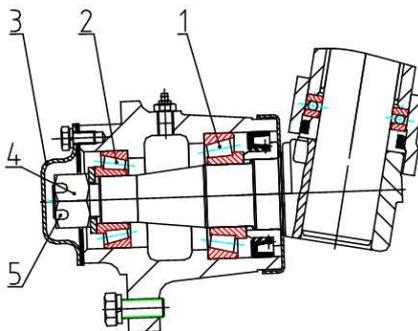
Регулировка осевого зазора подшипника переднего колеса
